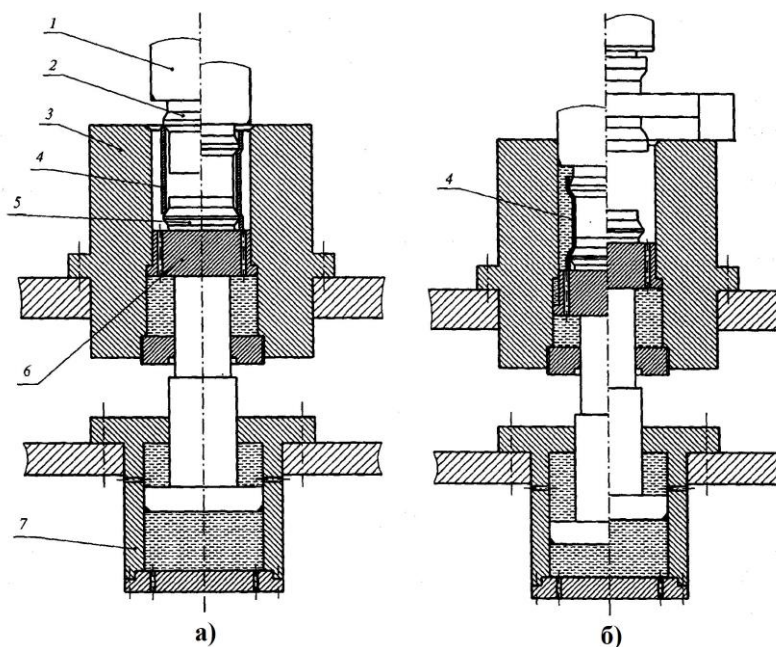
Конструкція установки для пластичної деформації циліндричних оболонок рідиною високого тиску: а – формування, б – калібрування
